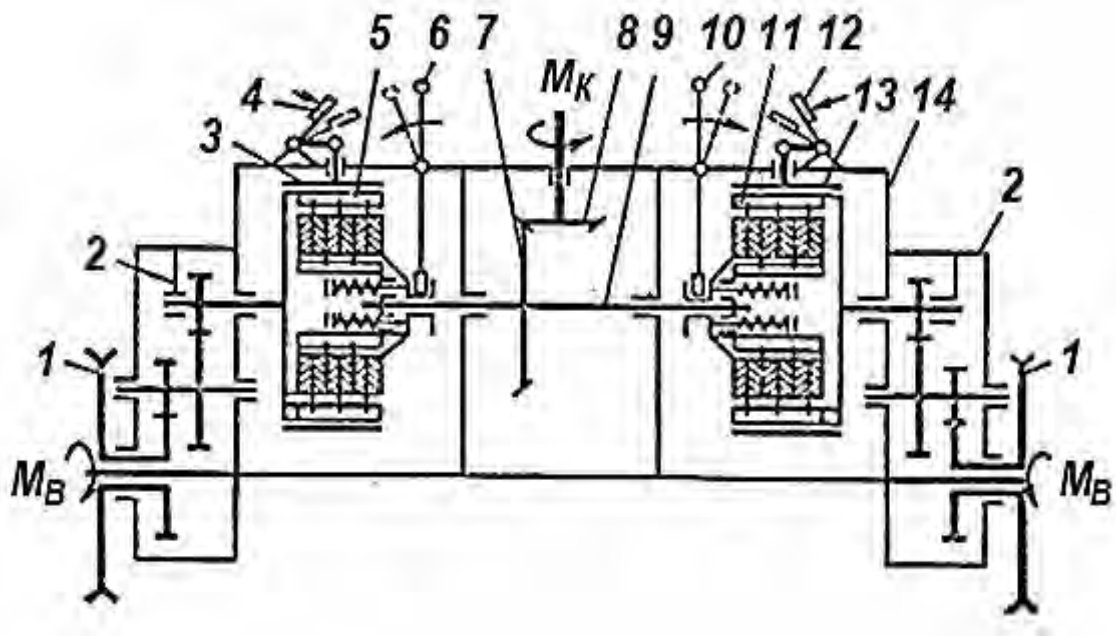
Ведучий міст гусеничної машини з фрикційним механізмом повороту:
